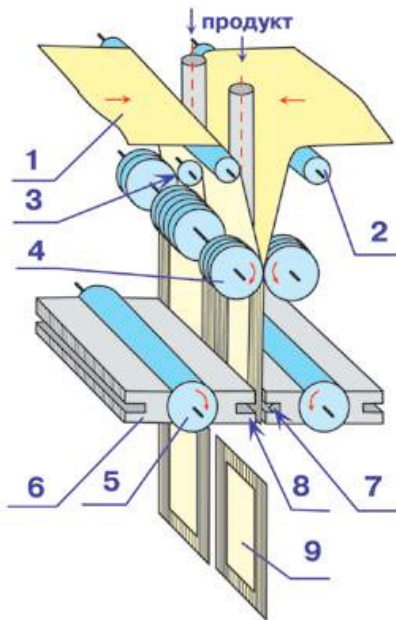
Компонування машини для пакування сипких речовин з губками зварювання і протяжки: 1 – плівка; 2 – ролики; 3 – ножі поздовжнього розрізання; 4 – ролики поздовжньої зварювання; 5 – ротори поперечної розрізання; 6 – губки поперечного зварювання; 7, 8 – відрізні ножі; 9 – готовий пакет
